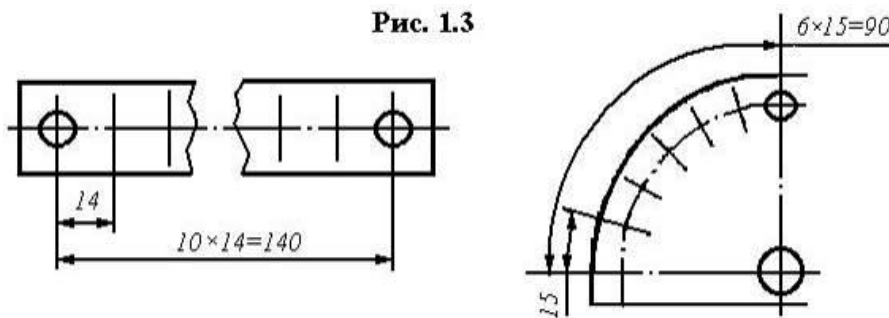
Размеры для равномерно расположенных одинаковых элементов
